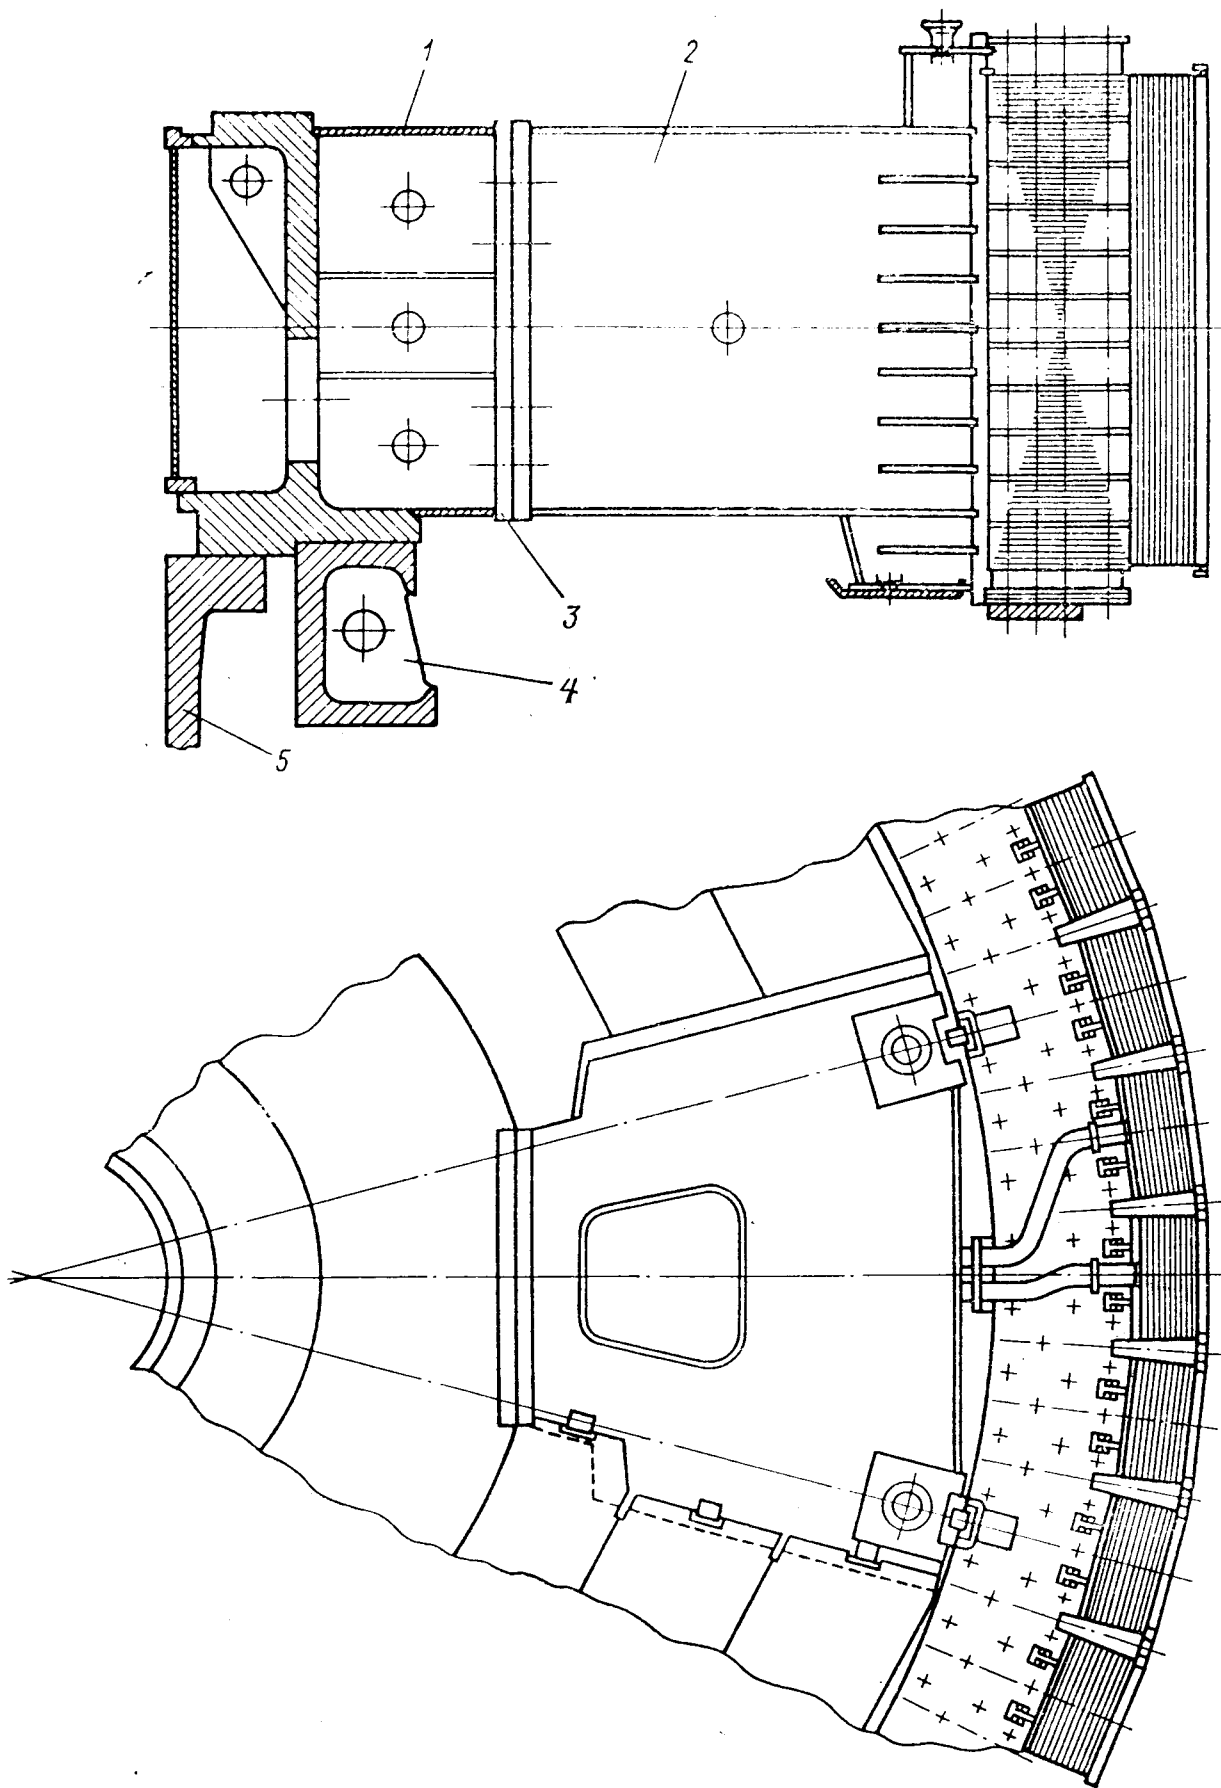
Ротор зонтичного гидрогенератора безвальневой конструкции с креплением спиц стыковыми плитами
